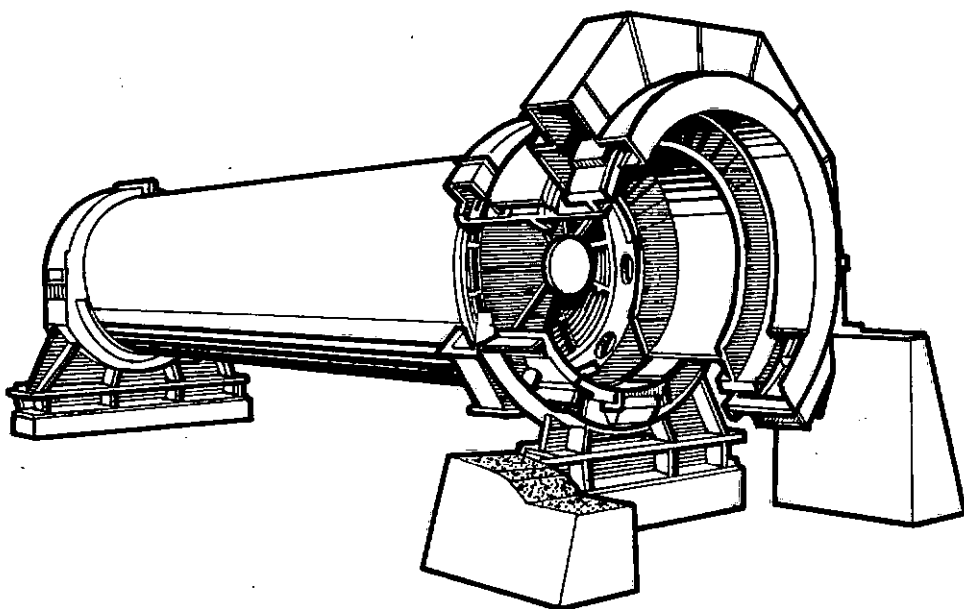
Moinho de bolas de corpo cilíndrico.
